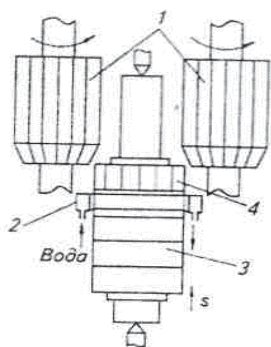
Схема накатки зубьев цилиндрических колес
